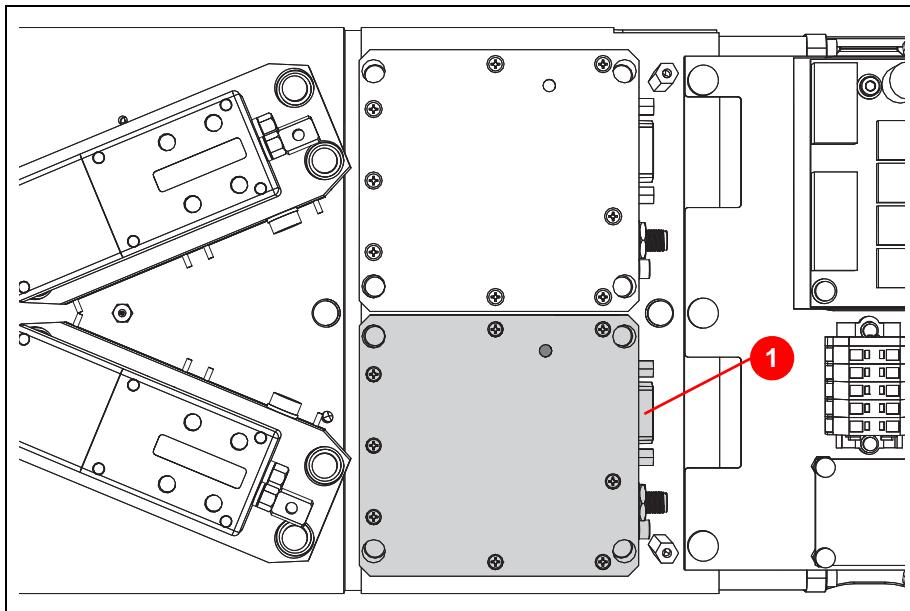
Anschlussstecker -X12 HG 29-80
